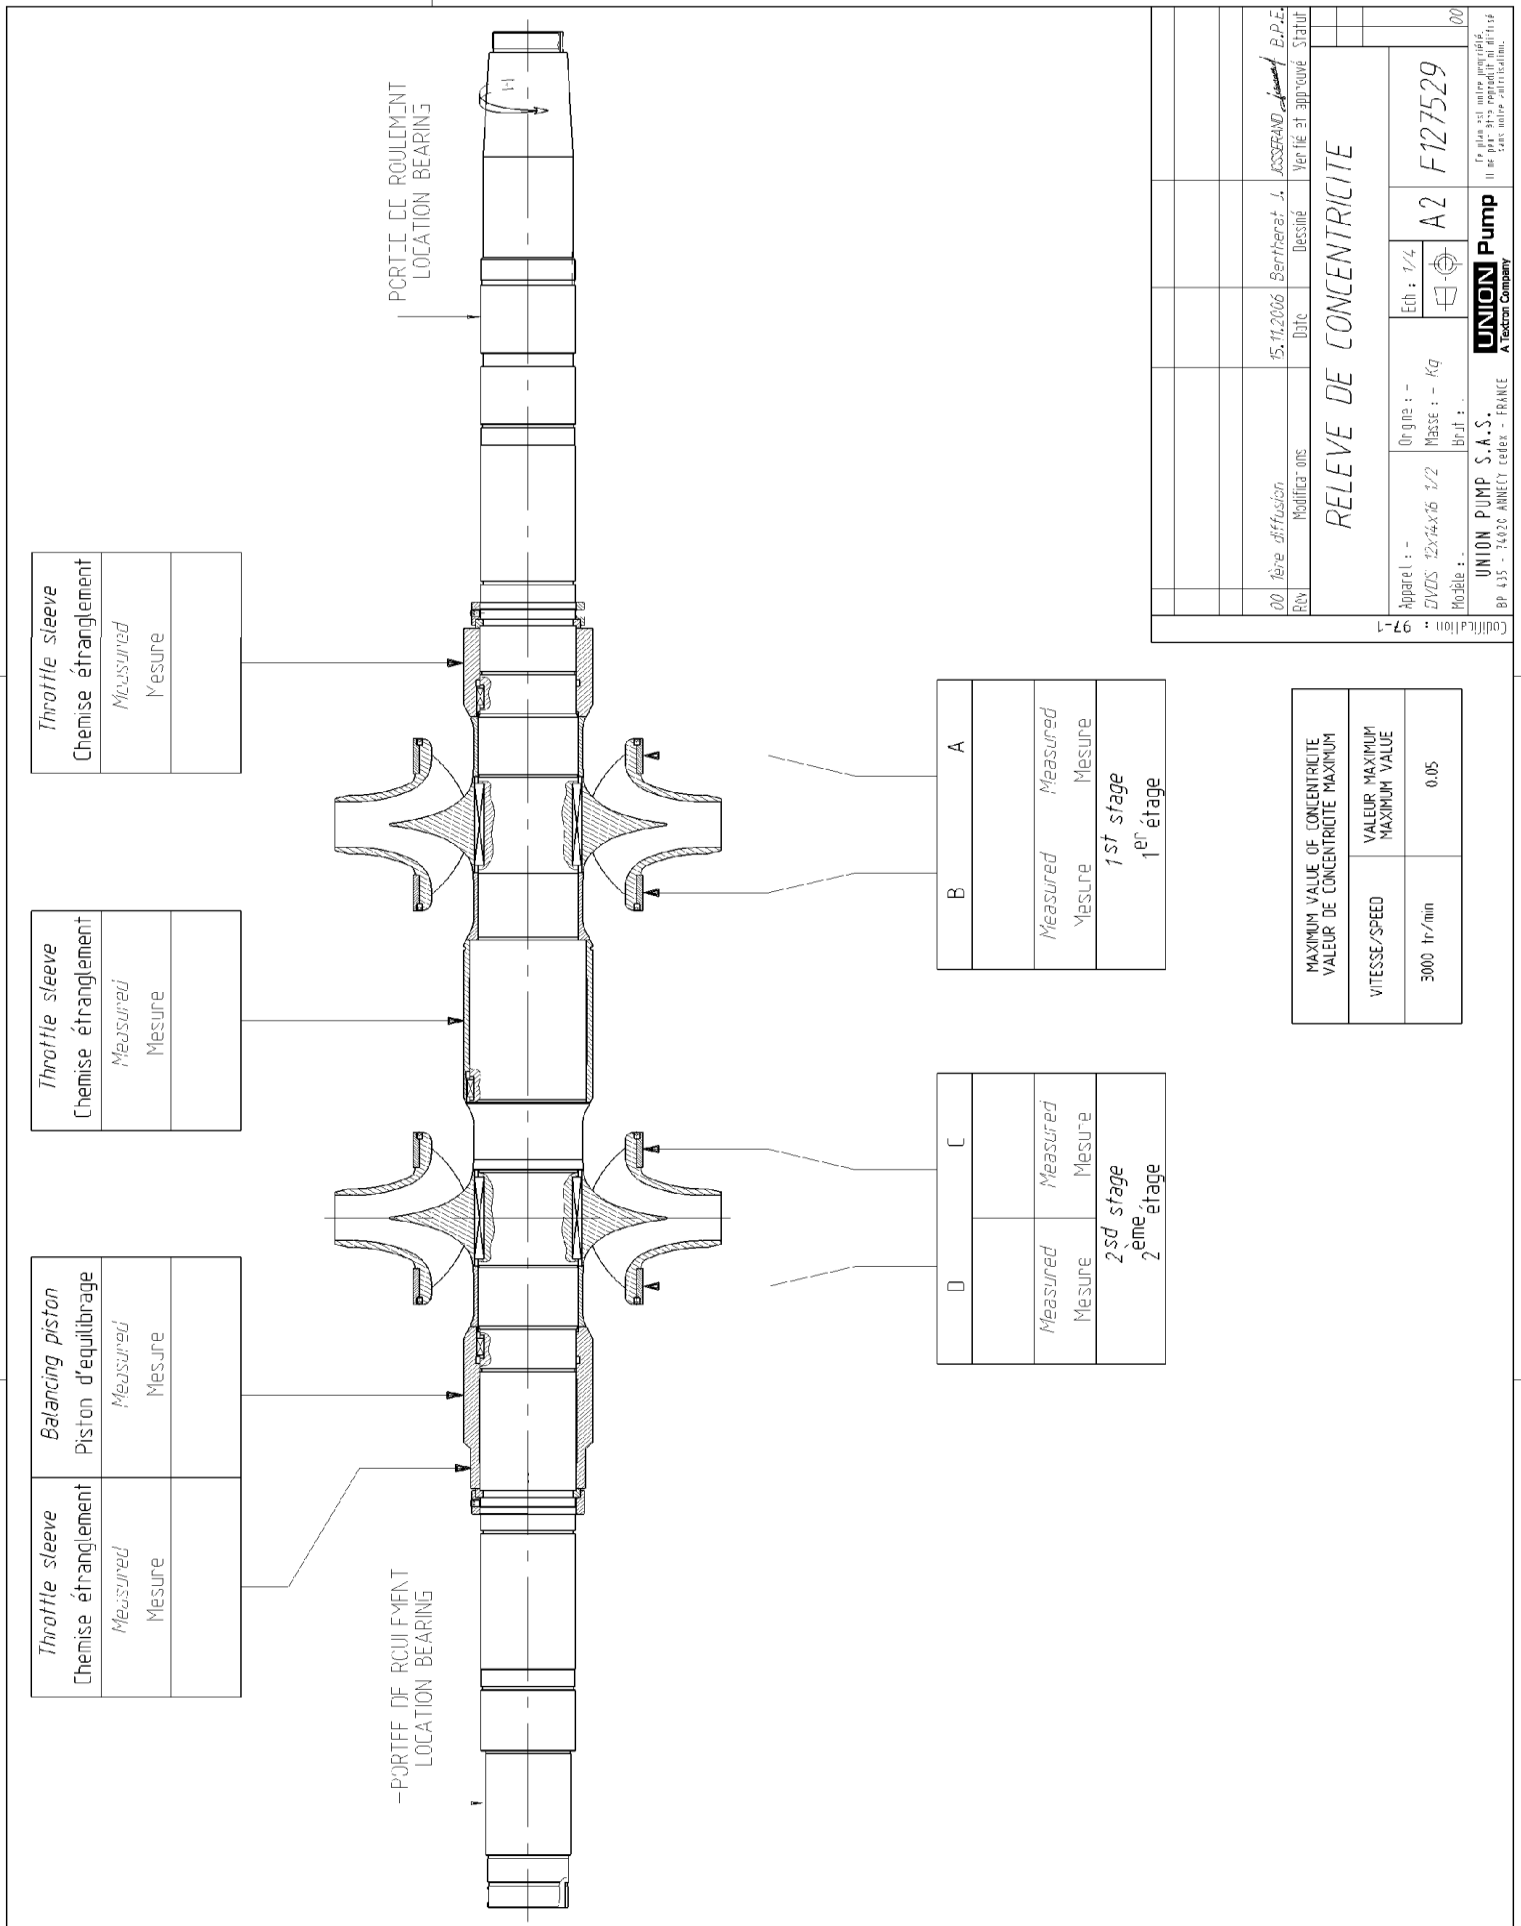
Dessin de définition de partie Mobile de pompe. [17]
